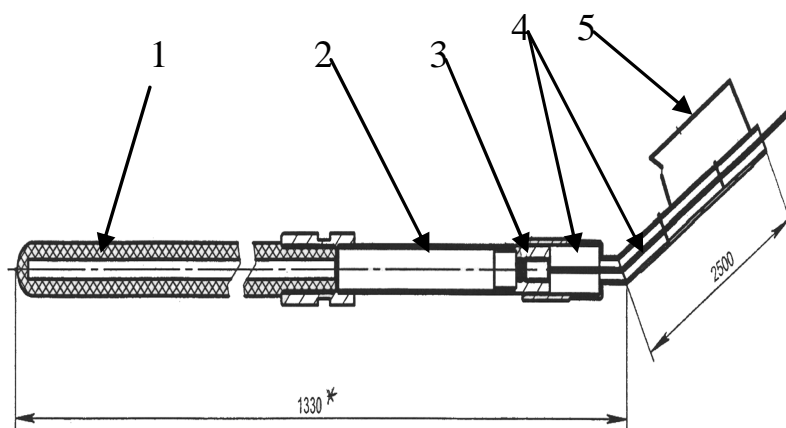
Варіант конструкції експериментальної установчої арматури із закритим зондом:
